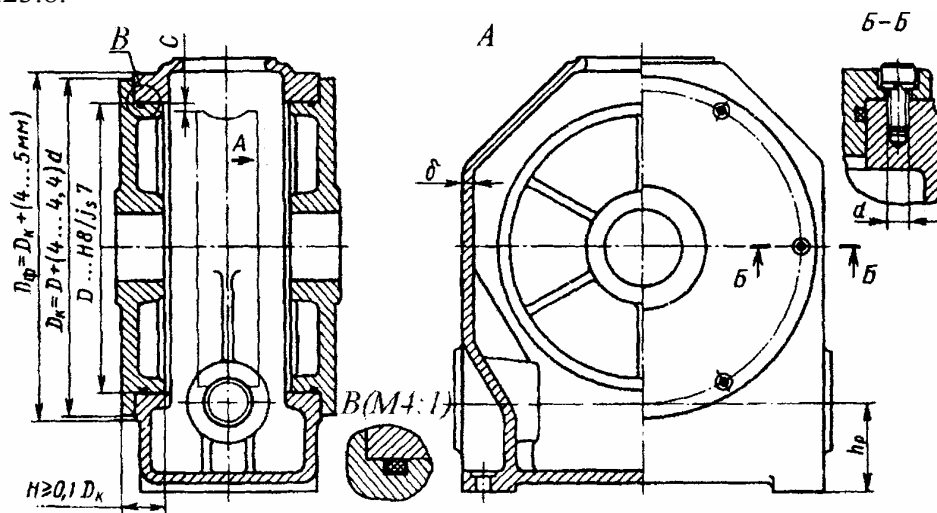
Цельнолитой корпус червячного редуктора с двумя окнами на боковых стенках
